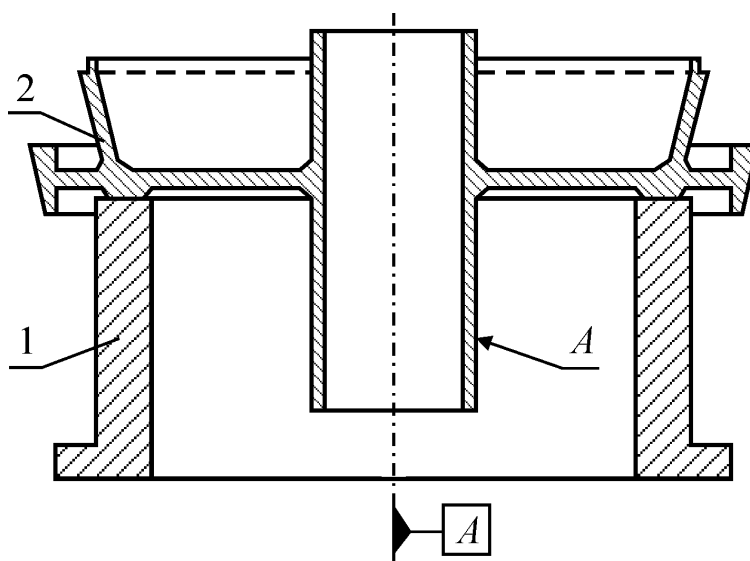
Установка на поворотный сборочный стапель (1) первого диска с валом (2)
